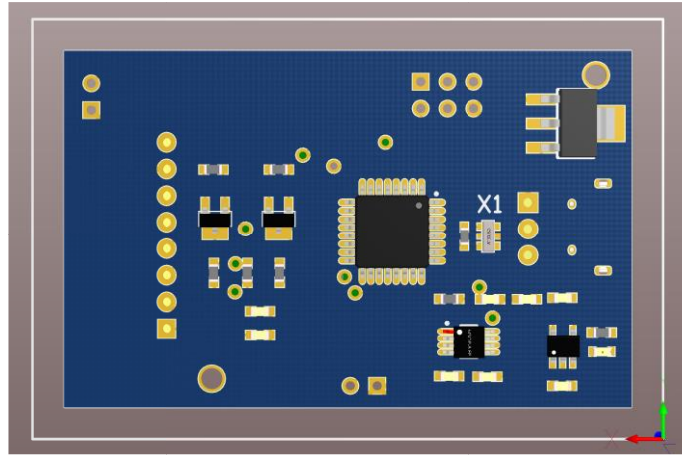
Resultado del PCB Final visto desde la Capa Inferior [20]
